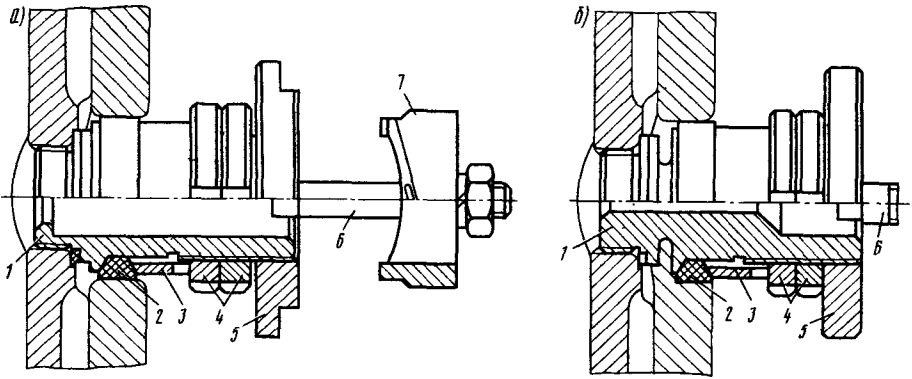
Адаптеры форсунки (а) и индикаторного крана (б) новой конструкции: 1 — корпус адаптера; 2 — резиновое кольцо; 3 — нажимная втулка; 4 — гайка; 5 — фланец; 6 — шпилька; 7 — центрирующий фланец
